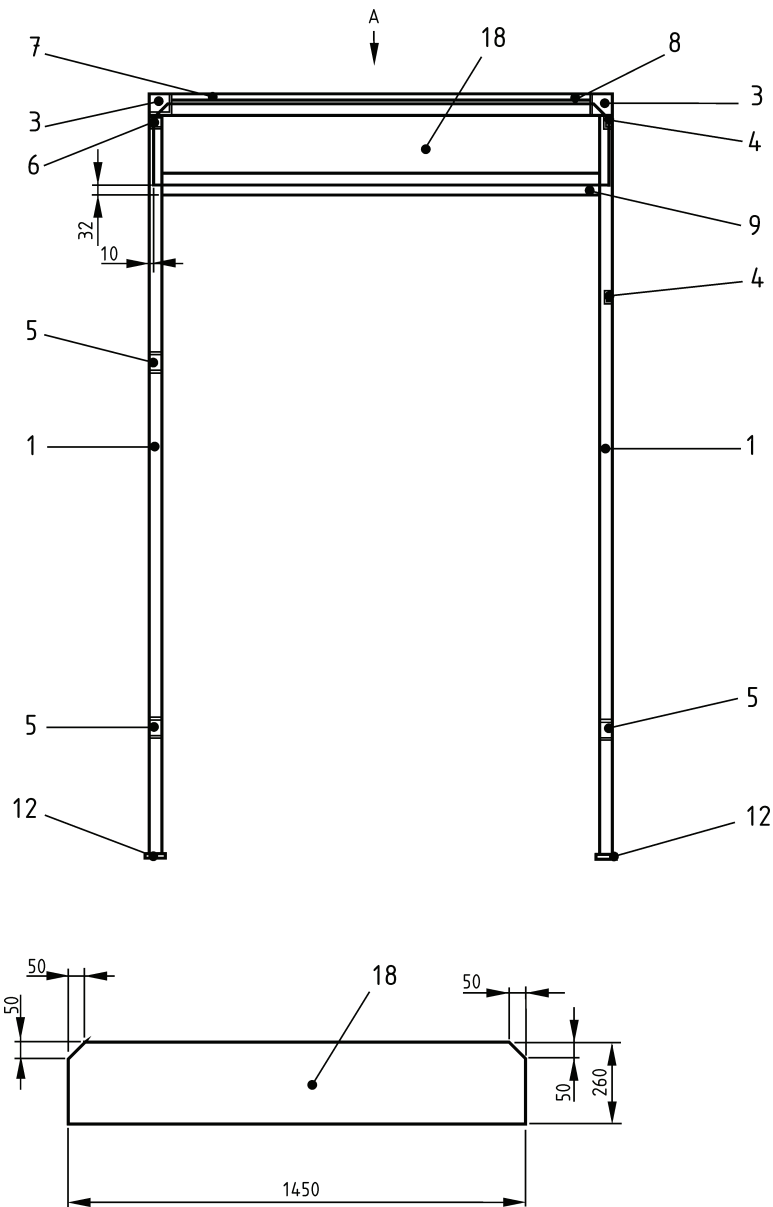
Rahmen, geschweißte Teile, Schnitt A und B
